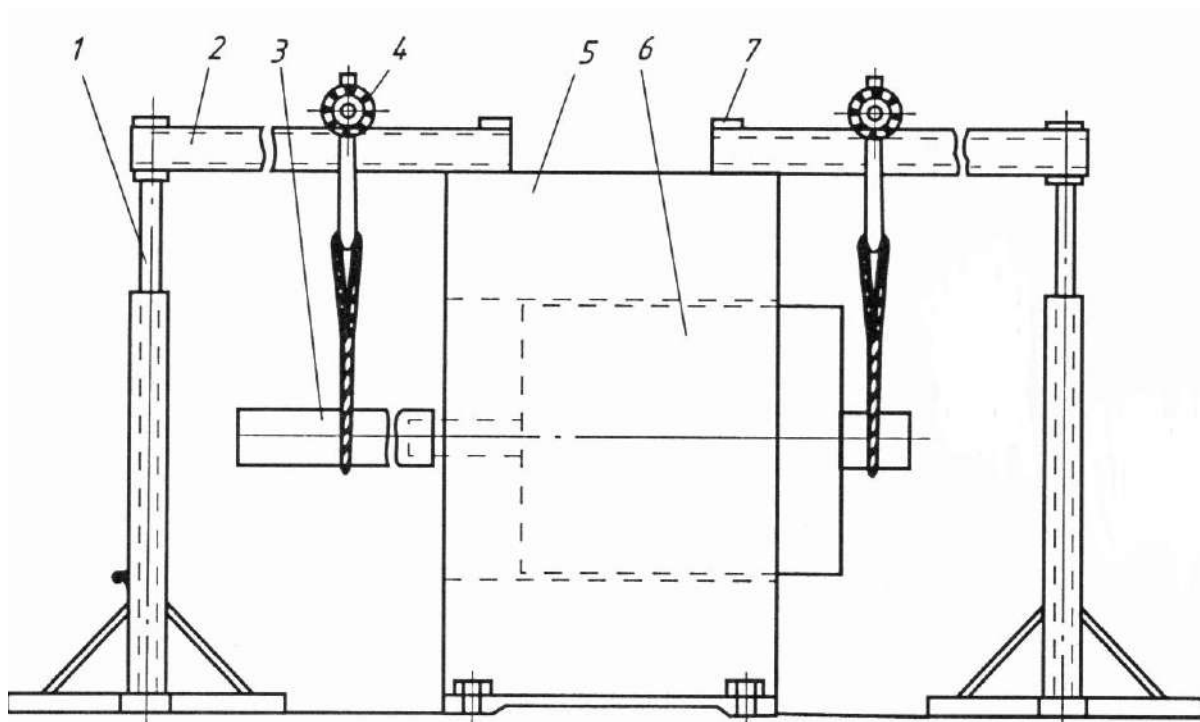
Схема ввода ротора в статор с применением удлинителя и специального приспособления: 1. – стойка; 2 – балка; 3 – удлинитель; 4 – грузовой ролик; 5 – статор; 6 – ротор; 7 – накладка
